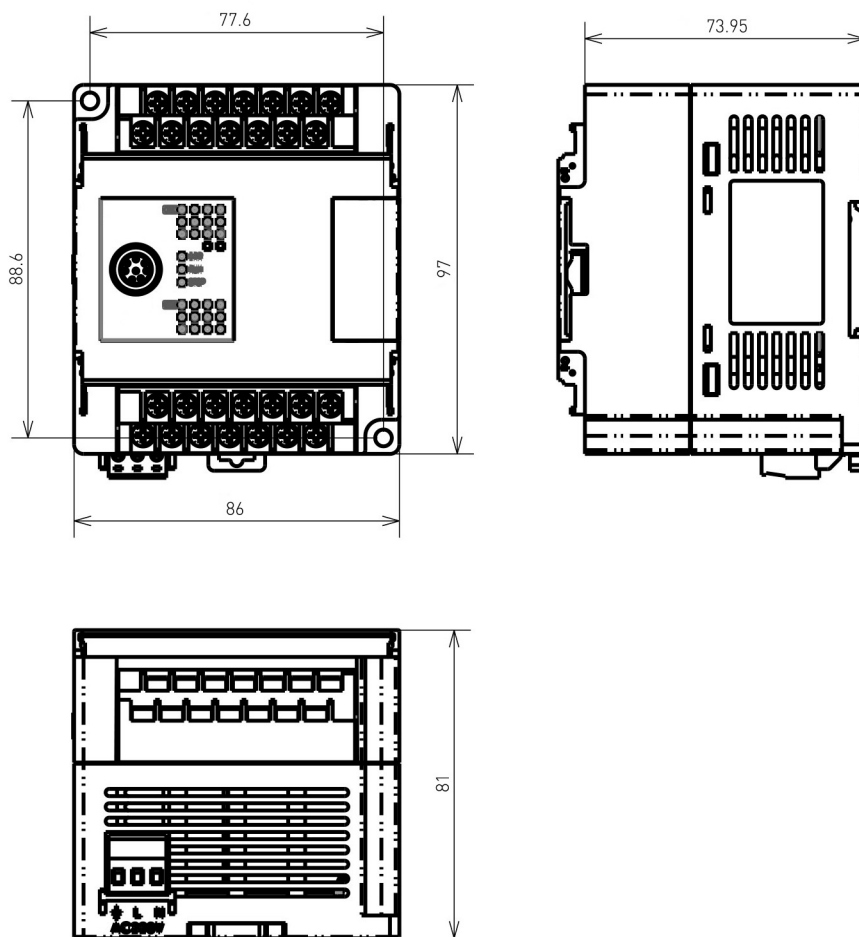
Габаритный чертеж PLC контроллера FAS-20MT-AC.
